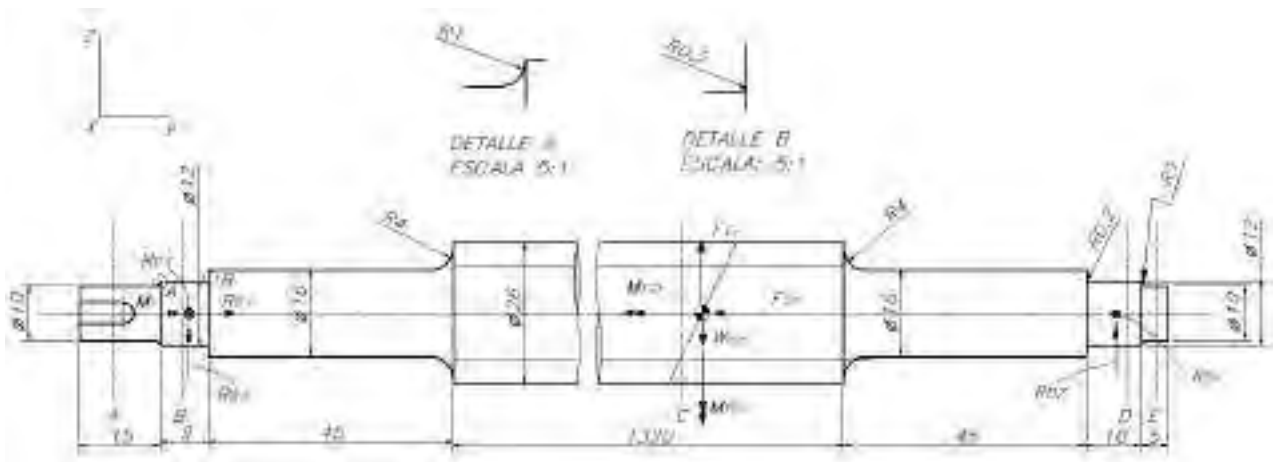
Medidas finales del eje giratorio en el plano Y-Z Fuente: Elaboración propia
